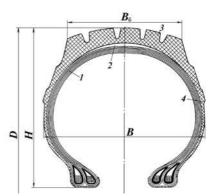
Основные конструктивные элементы и размеры шины: 1 -каркас; 2 -брекер; 3 -протектор; 4 -боковина
